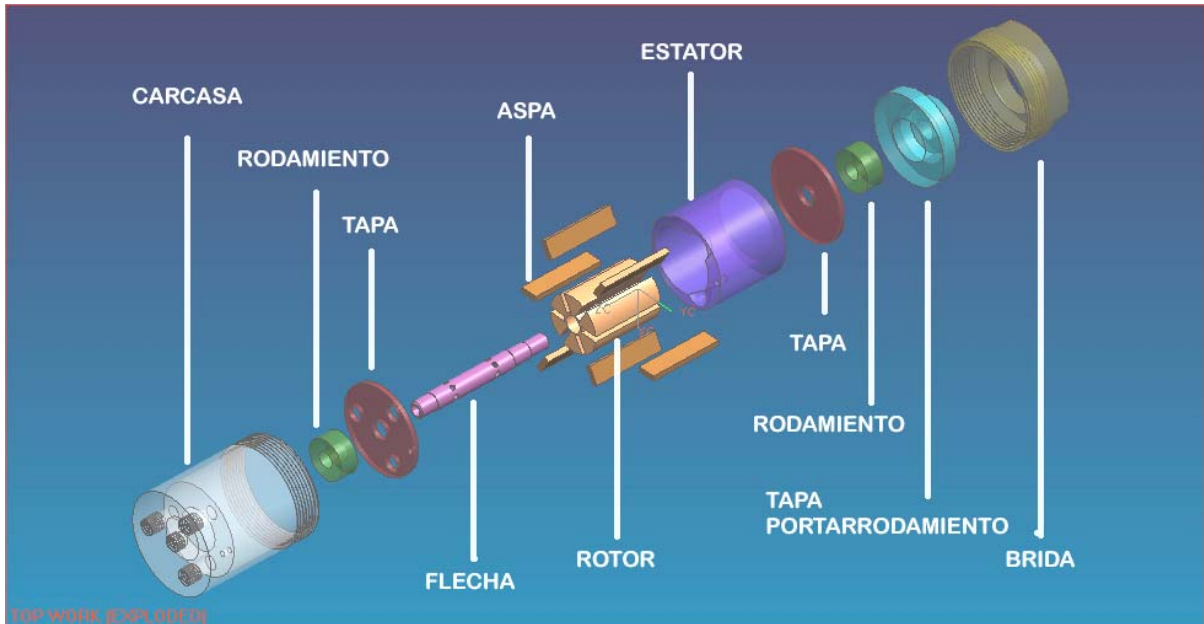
Ensamble explosivo del micromotor neumático de aspas diseñado por el GMM, del CCADET.
